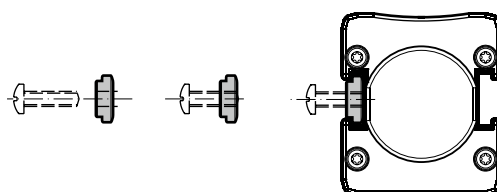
MONTAGE MIT BEFESTIGUNGSMUTTER UND M5-SCHRAUBE
